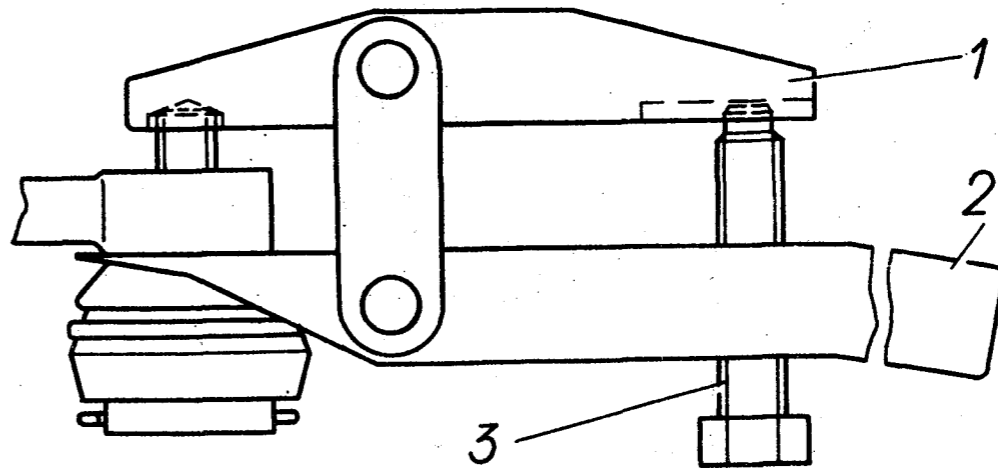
Выпрессовка пальца шарового шарнира из поворотных рычагов и бобышек тяги сошки:
